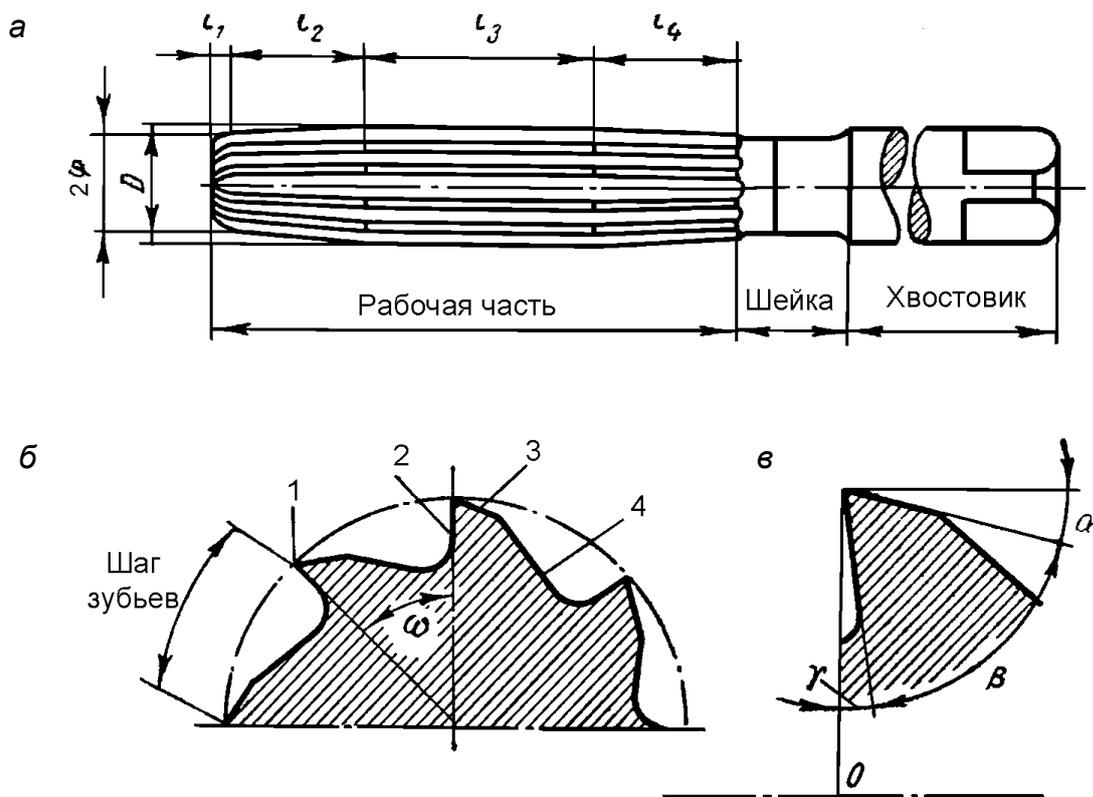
Развертка, ее части и элементы: 1 – главная режущая кромка; 2 – передняя поверхность; 3 – затылочная поверхность; 4 – задняя поверхность
